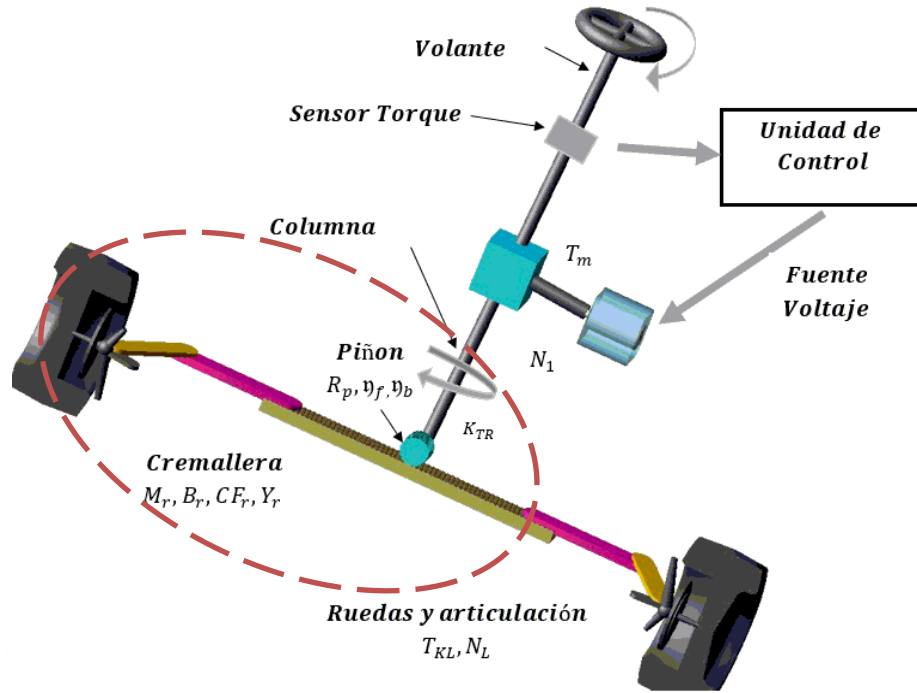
Conjunto Piñón-Cremallera [Adams/View]
